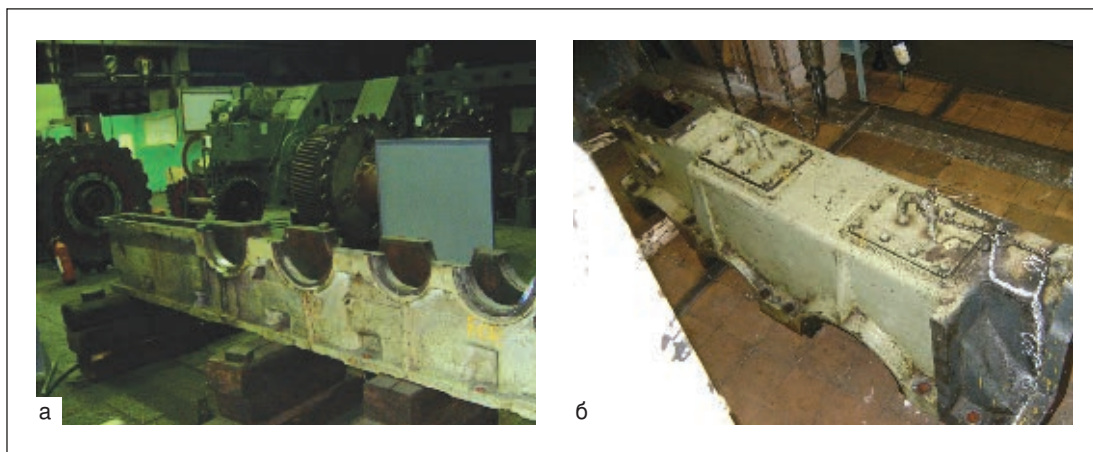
Общий вид корпуса редуктора до ремонта: а — основание; б — крышка
